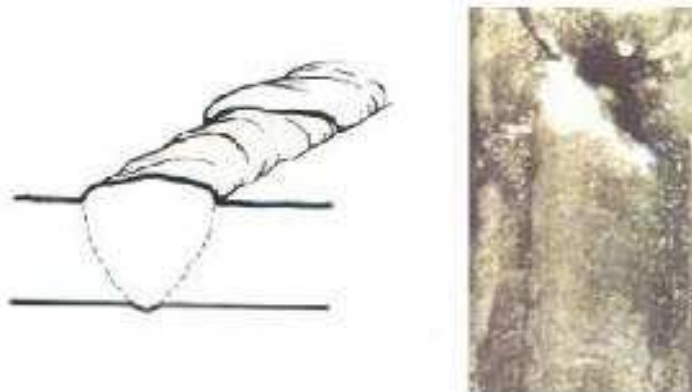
Falta de continuidad en el cordón de soldadura.
